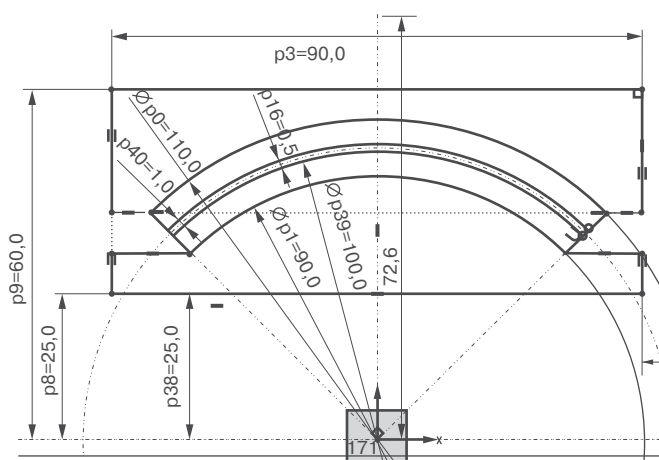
Главный эскиз для построения геометрической модели шарнира:
